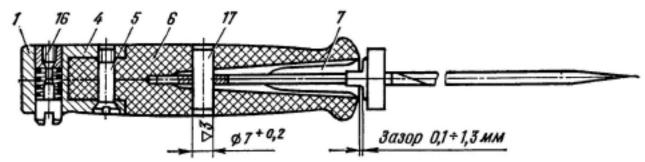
Замена рукоятки штыка-ножа: 1 — пружина защелки; 4 — наконечник; 5 — винт; 6 — рукоятка штыка-ножа; 7 — штык-нож в сборе; 16 — винт защелки; 17 — стержень
